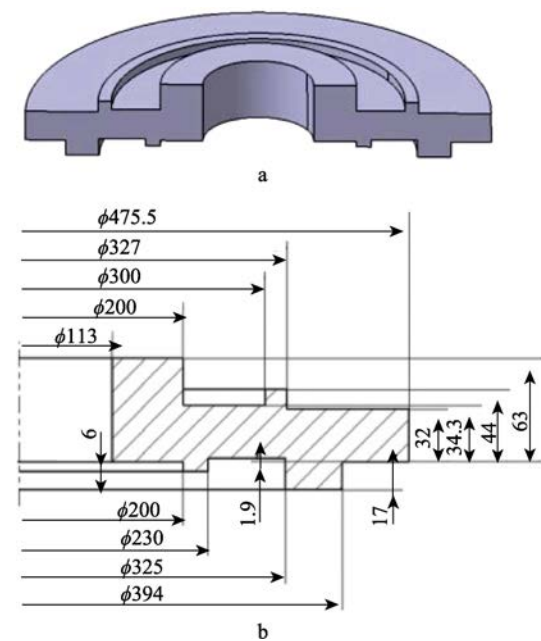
GH901 合金涡轮盘锻件粗加工尺寸图
